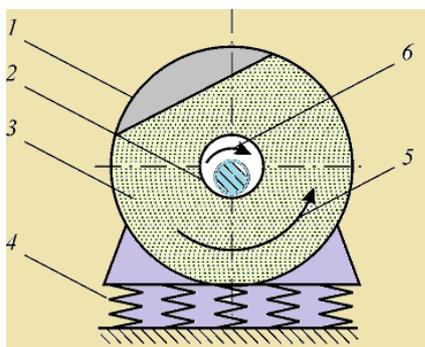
Схема вибрационной мельницы с внутренним эксцентриковым валом: 1 - корпус мельницы; 2- эксцентриковый (или дебалансный) вал; 3 – шаровая загрузка с измельчаемым материалом; 4 – пружинные опоры; 5 – направление циркуляции загрузки; 6 – направление движения вала
